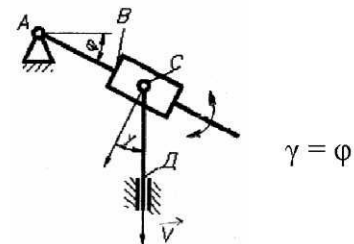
Тангенсный механизм (кулисный с ведущей кулисой)
